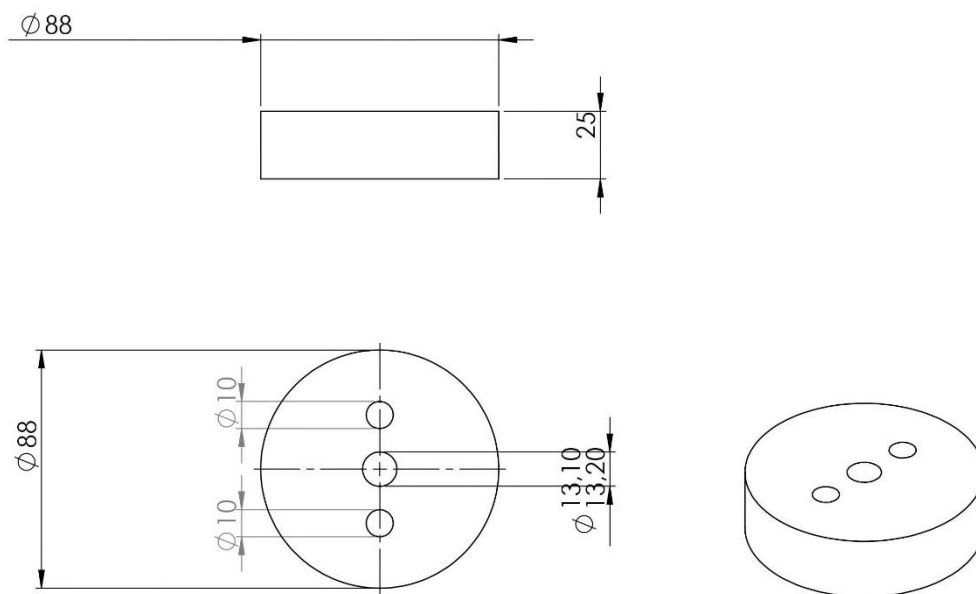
Desenho técnico da peça matriz do conjunto de prensagem.
